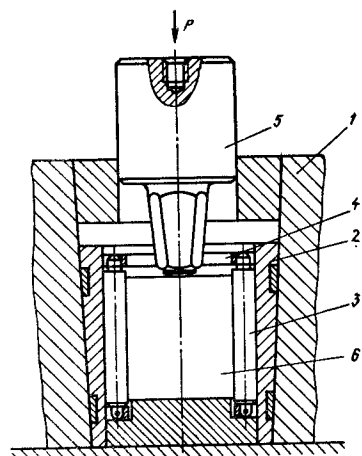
Пакет-штамп с роликовой кассетой для выдавливания глубоких полостей матриц пресс-форм:
